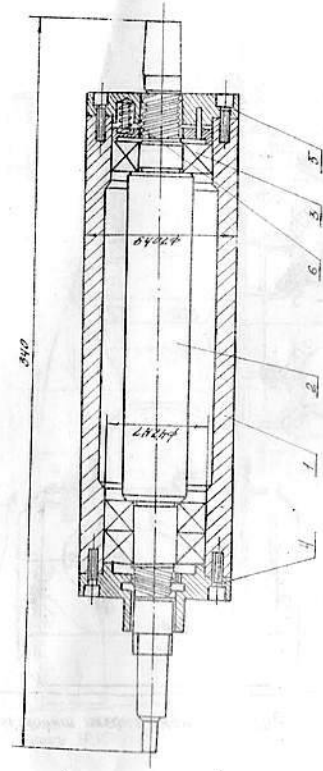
Шиндель фрезы гелема машины ФУП-3-0.
